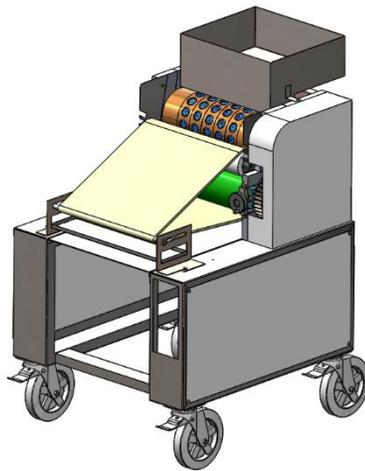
Vue de la machine mouleuse rotative à biscuit
